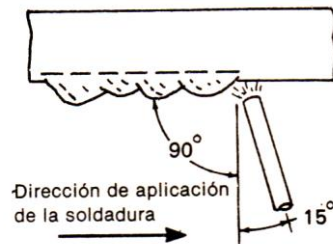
Dirección de aplicación del cordón de soldadura en la posición sobrecabeza.
